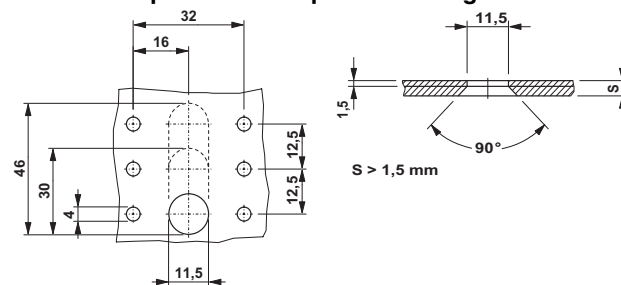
Abmessungen (in mm) für 1-, 2- und 3-polige Schutzschalter
